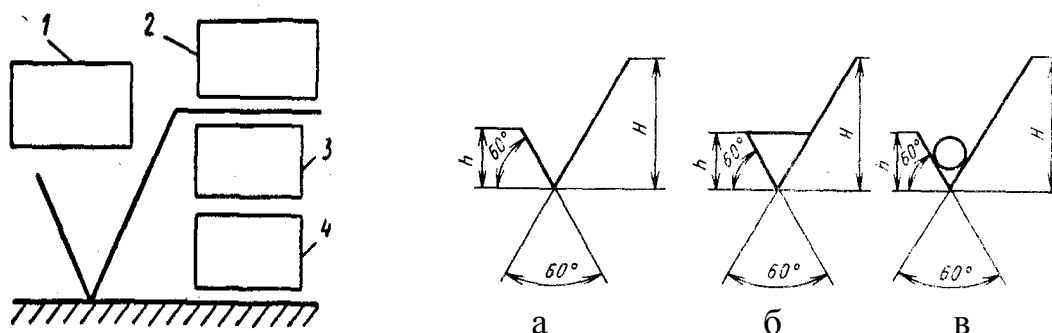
Знаки для обозначения шероховатости: 1- параметр шероховатости поверхности; 2 – вид обработки поверхности; 3 – базовая линия по ГОСТ; 4 – условное обозначение направления неровностей; а - вид обработки конструктор не устанавливает; б - при удалении слоя материала; в - без удаления слоя материала.
